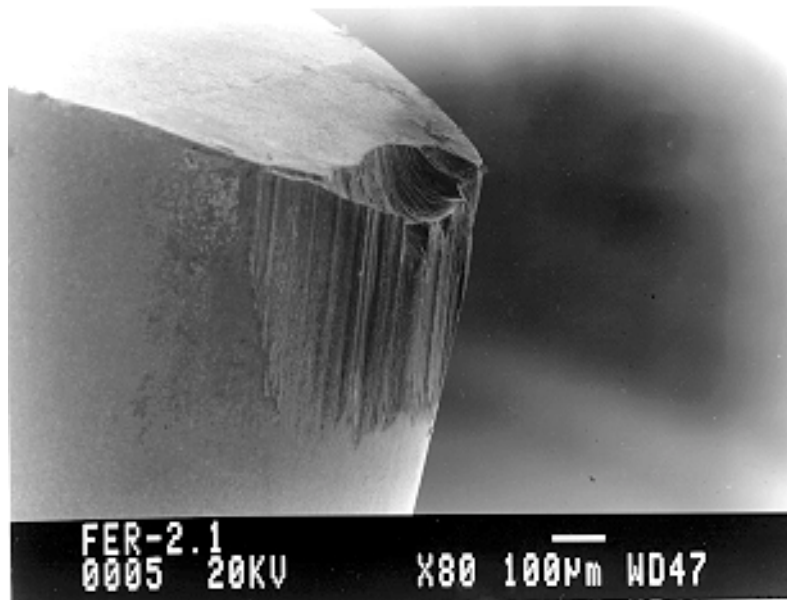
Forma de desgaste da ferramenta de PCBN. $v_c = 108$ m/min.
